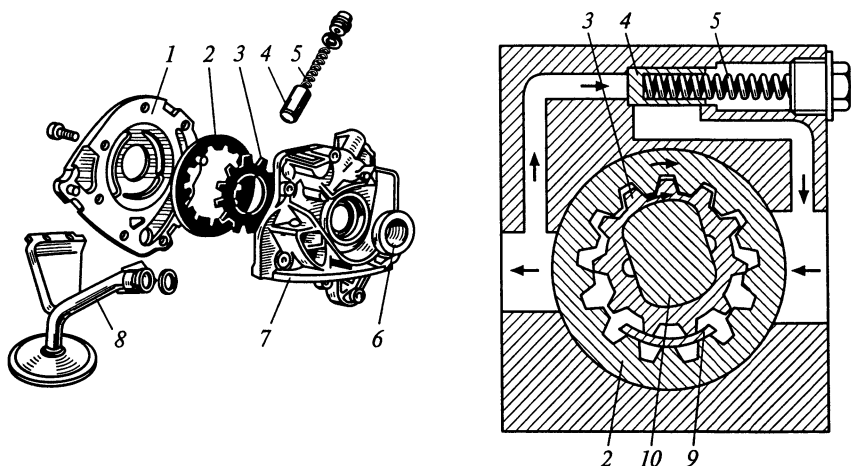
Масляный насос с шестернями внутреннего зацепления:
